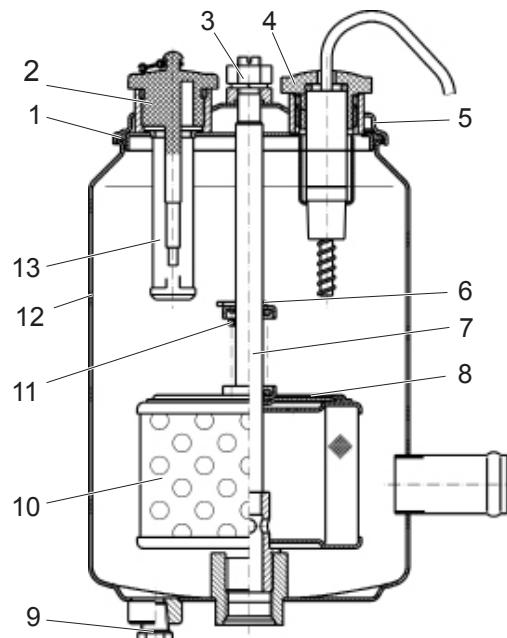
Масляный бак гидроусилителя рулевого управления
